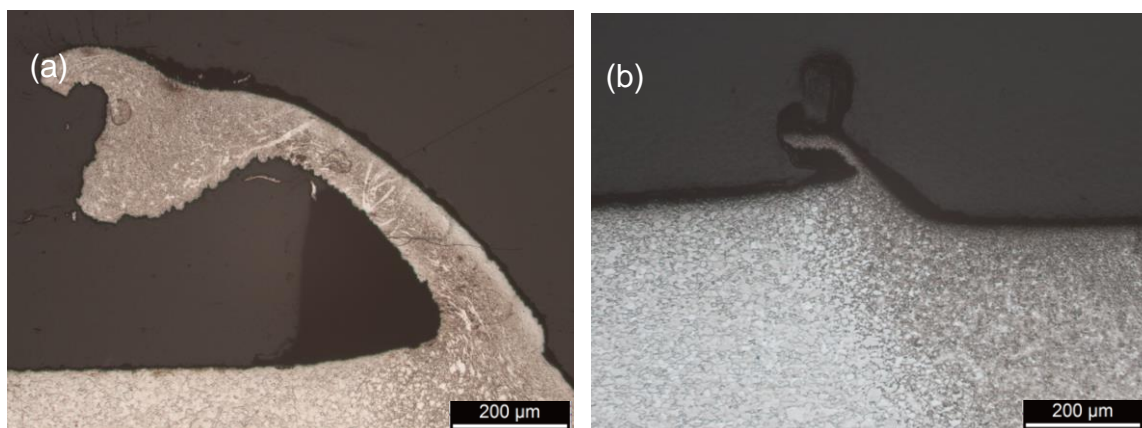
Macrografias da seção transversal das diferentes condições soldadas do aço AISI 410S.
